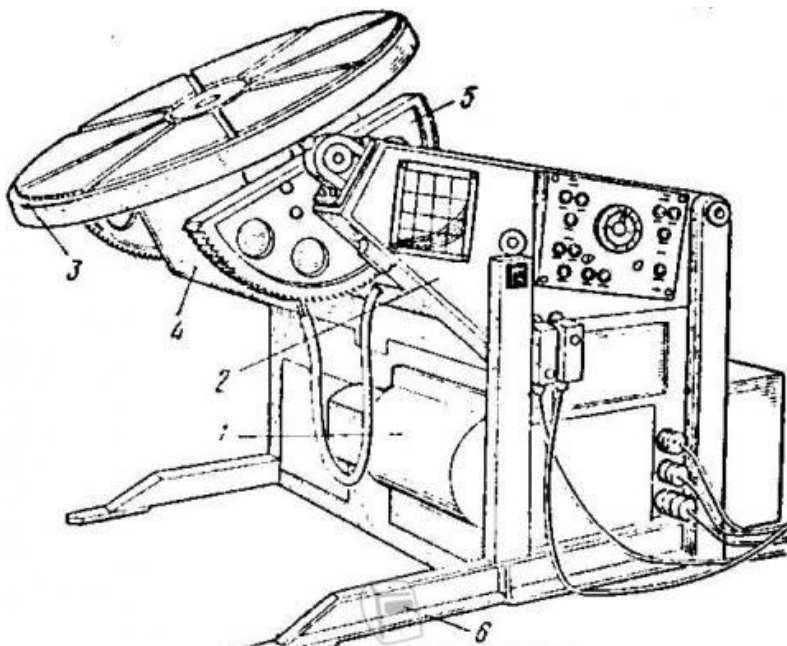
Универсальный сварочный манипулятор
